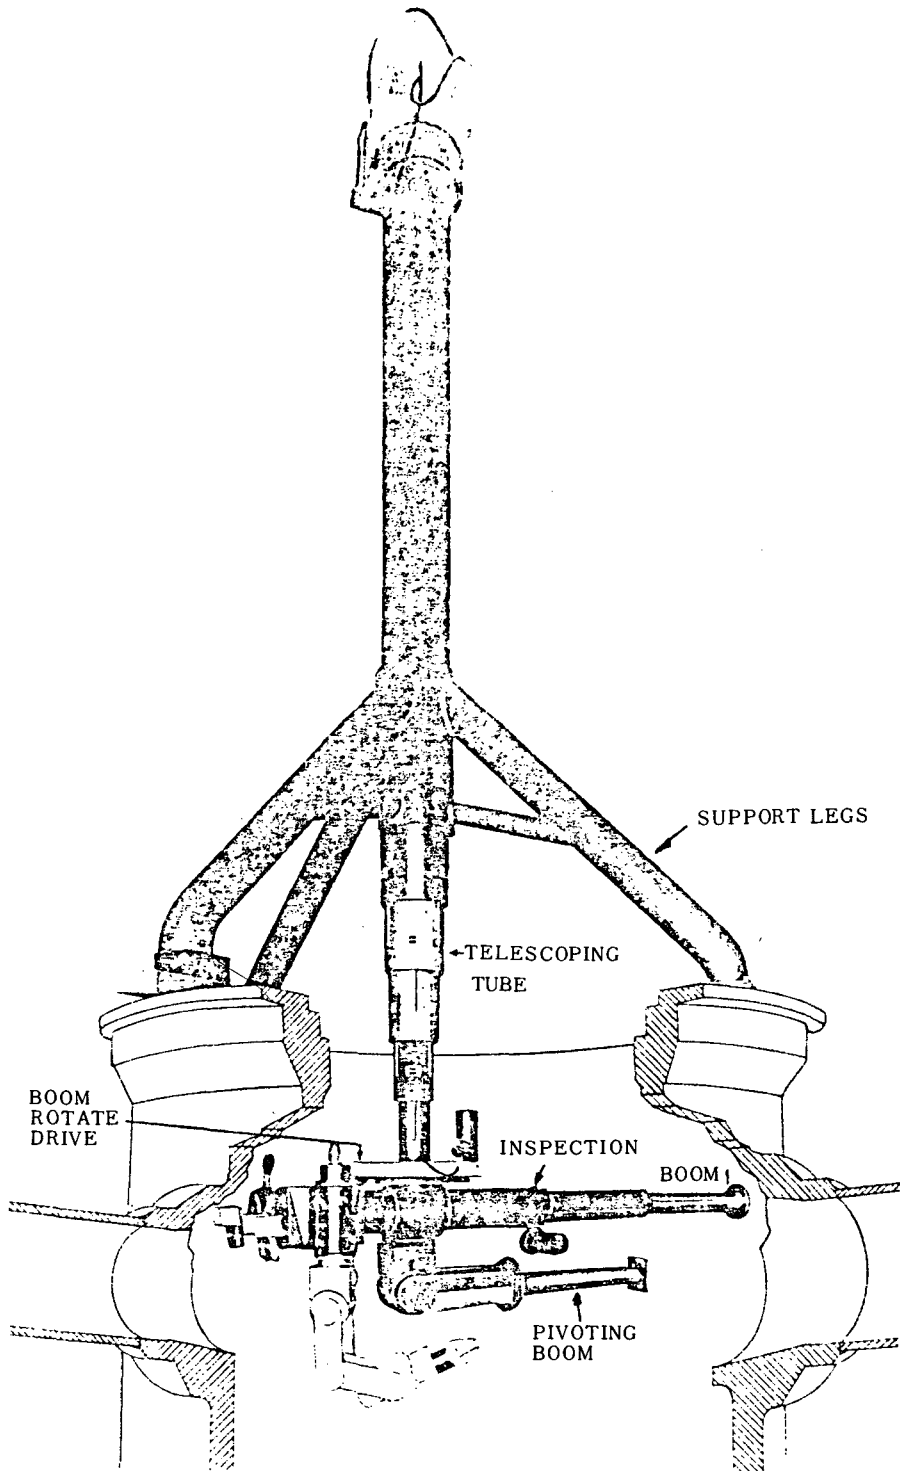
Model ISI-2 In-Service Inspection System
